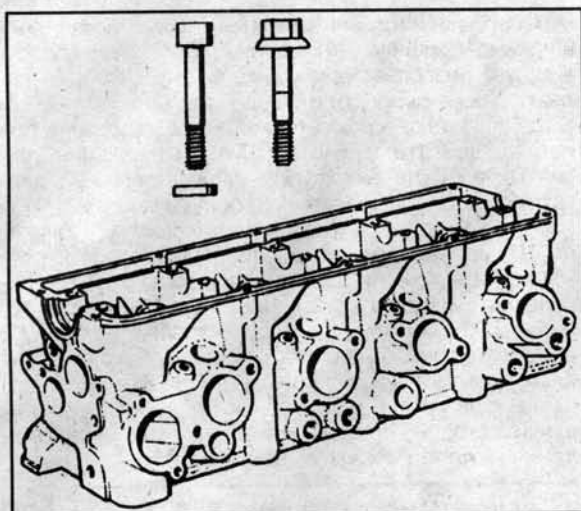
Головка блока цилиндров двигателя В19
